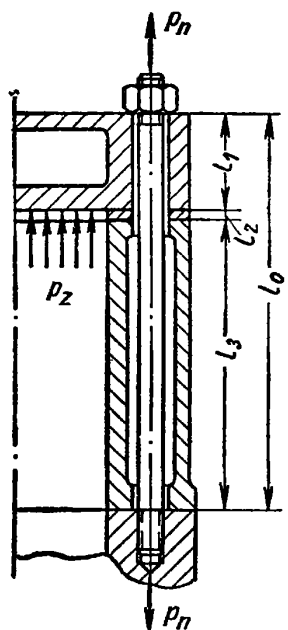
Схема крепления отъемной головки (крышки) двигателя с блоком цилиндра.
